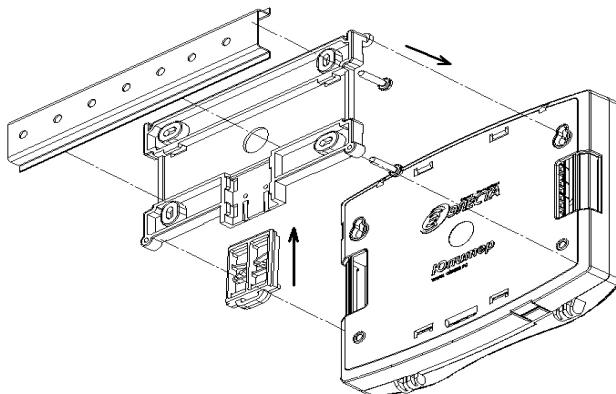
Вариант установки прибора через переходную планку на DIN-рейку(вид с задней крышки прибора)
